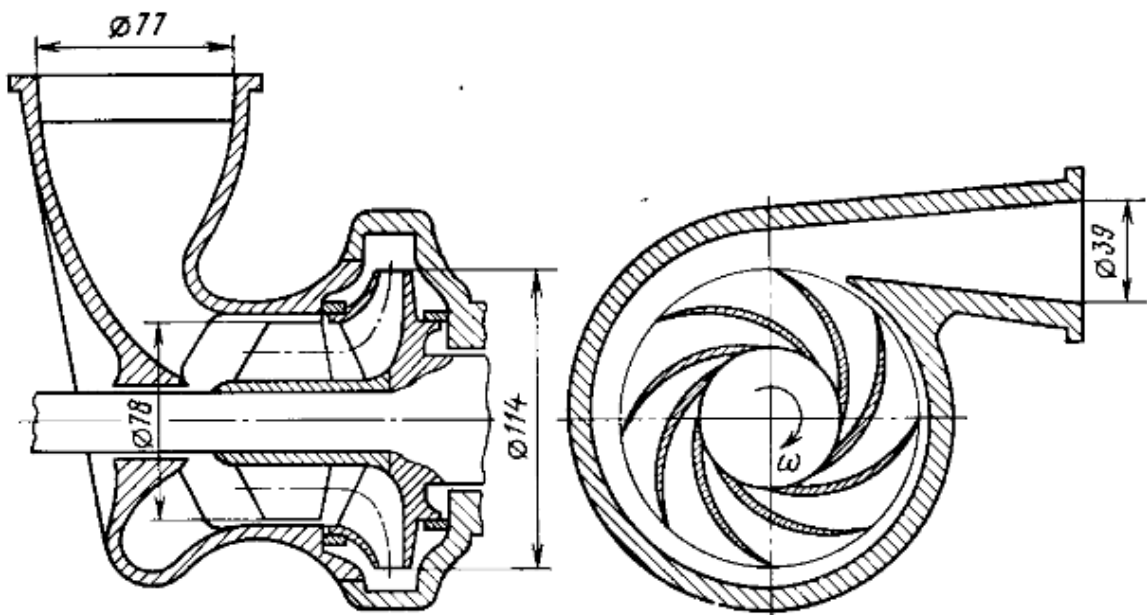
Конструктивный чертеж подкачивающего насоса
